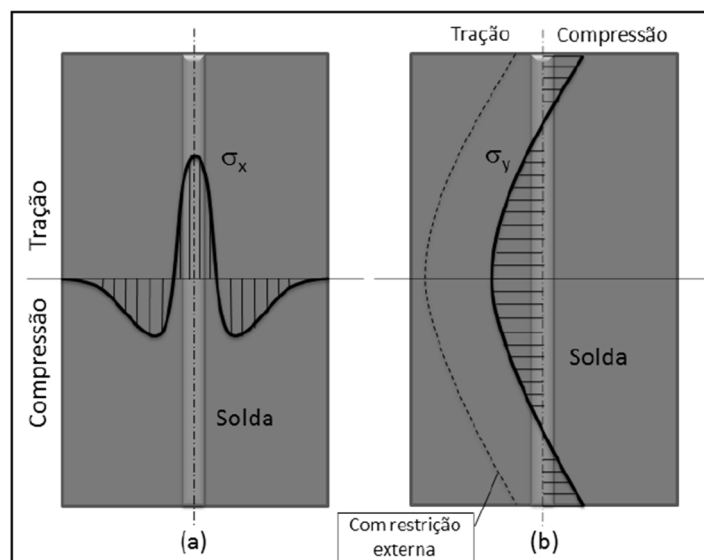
Distribuição típica das tensões longitudinais (σ_x) e transversais (σ_y) em uma junta a topo de um aço de baixo carbono (MASUBUCHI, 1980).
